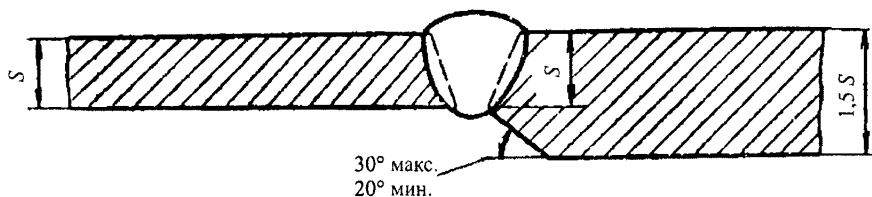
Конструктивные размеры разделки кромок и сварных швов разнотолщинных труб (до 1,5 толщины стенки)
